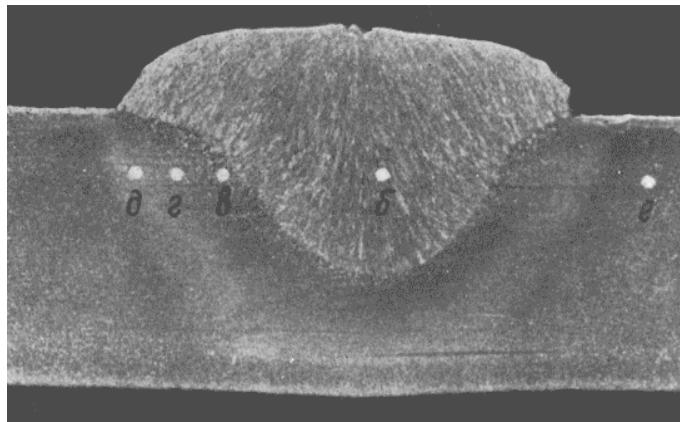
Макроструктура сварного шва стали Ст.3, выполненного электродуговой сваркой под флюсом, электродная проволока Св-08: б – сварной шов; в – участок перегрева; г - участок мелкого зерна; д – участок неполной перекристаллизации.
